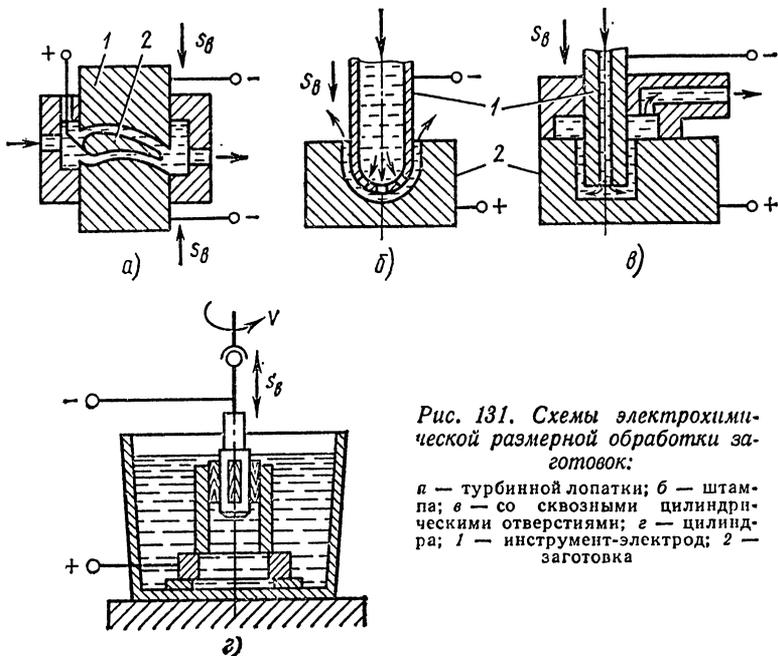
Схемы электрохимической размерной обработки заготовок:
